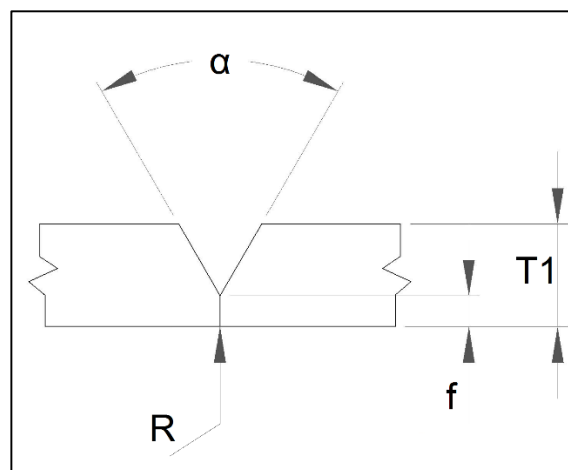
PJP - Soldadura de Canal Simple-V, Junta a Tope (B)
